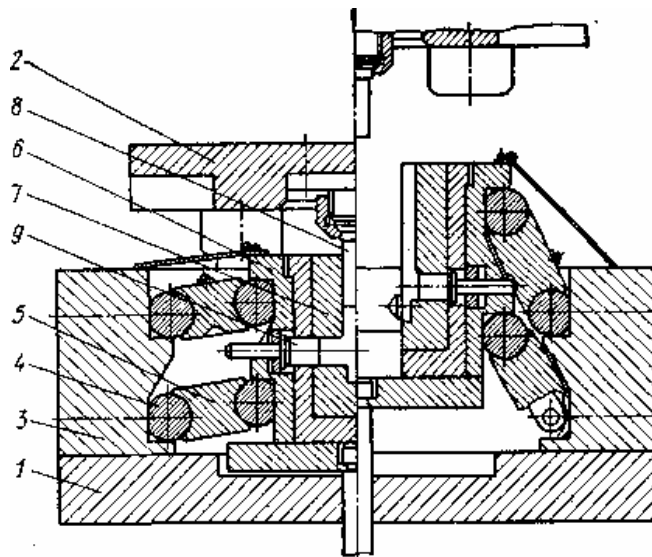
Ковочный пакет с вертикальным разъемом матриц
